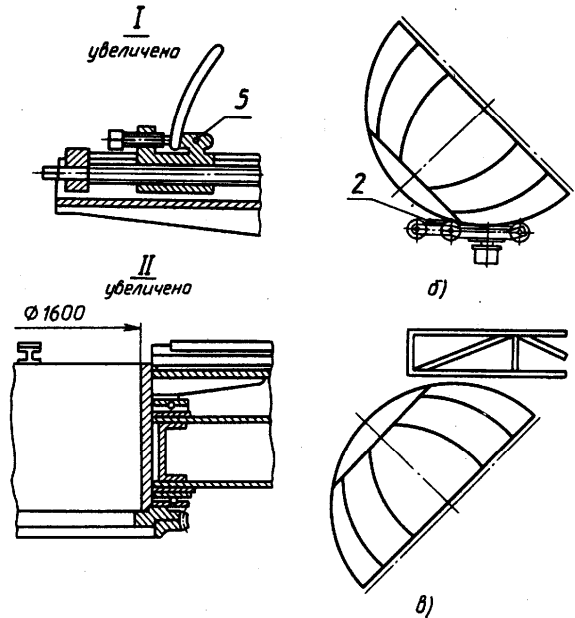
Стенд для автоматической сварки полусферических днищ
